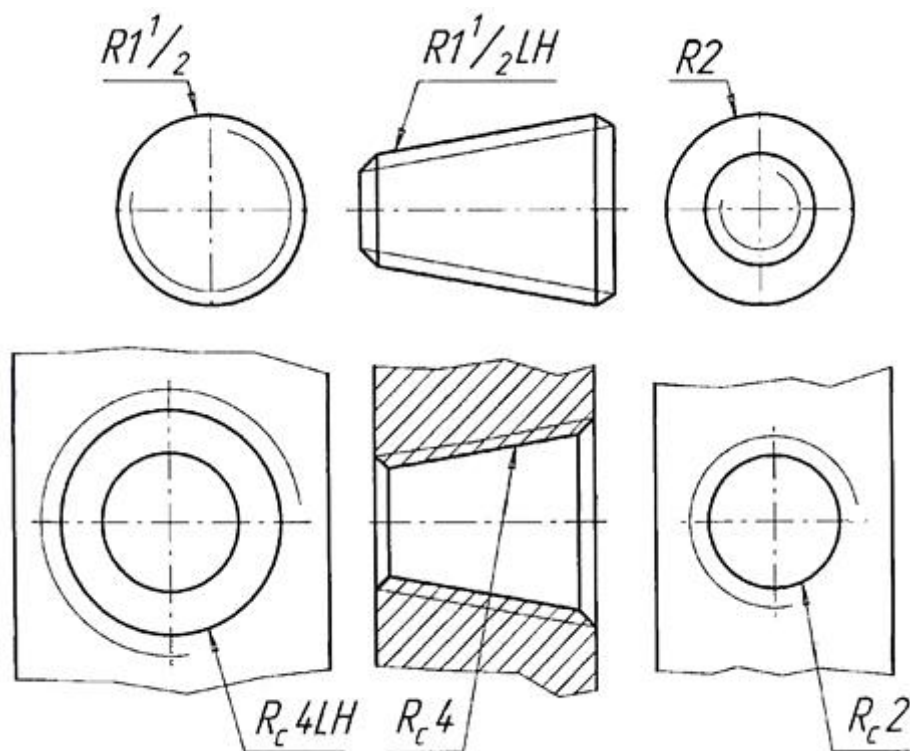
Обозначения трубной конической резьбы на чертежах
